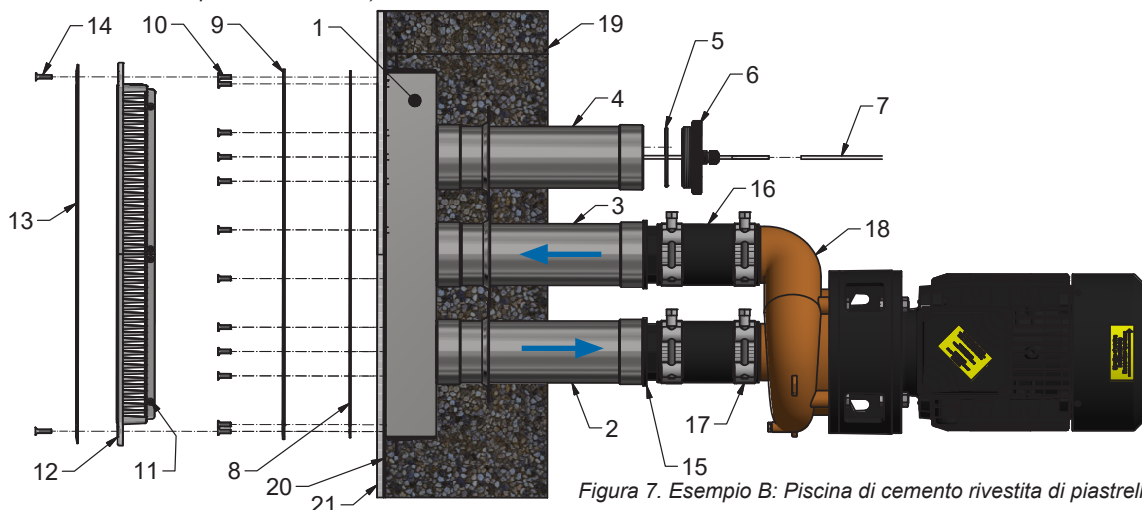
Esempio B: Piscina di cemento rivestita di piastrelle vista dall'alto
